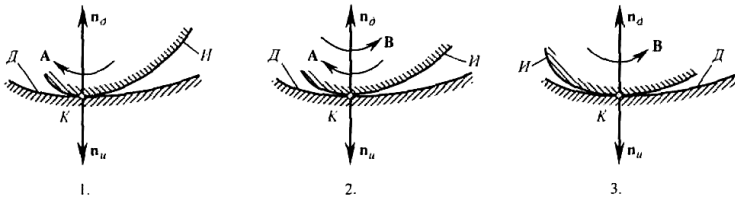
Зміна рухами орієнтування другого роду положення інструменту відносно деталі.
